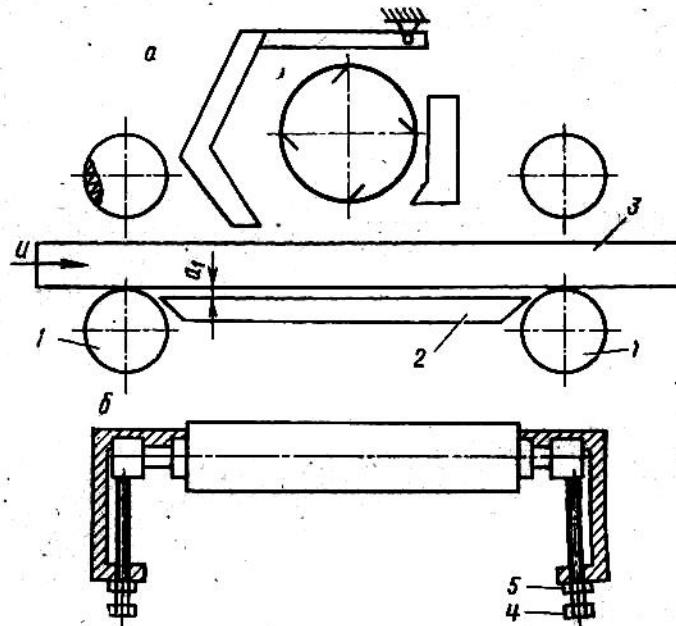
Схема наладки нижних опорных валиков рейсмусового станка:
